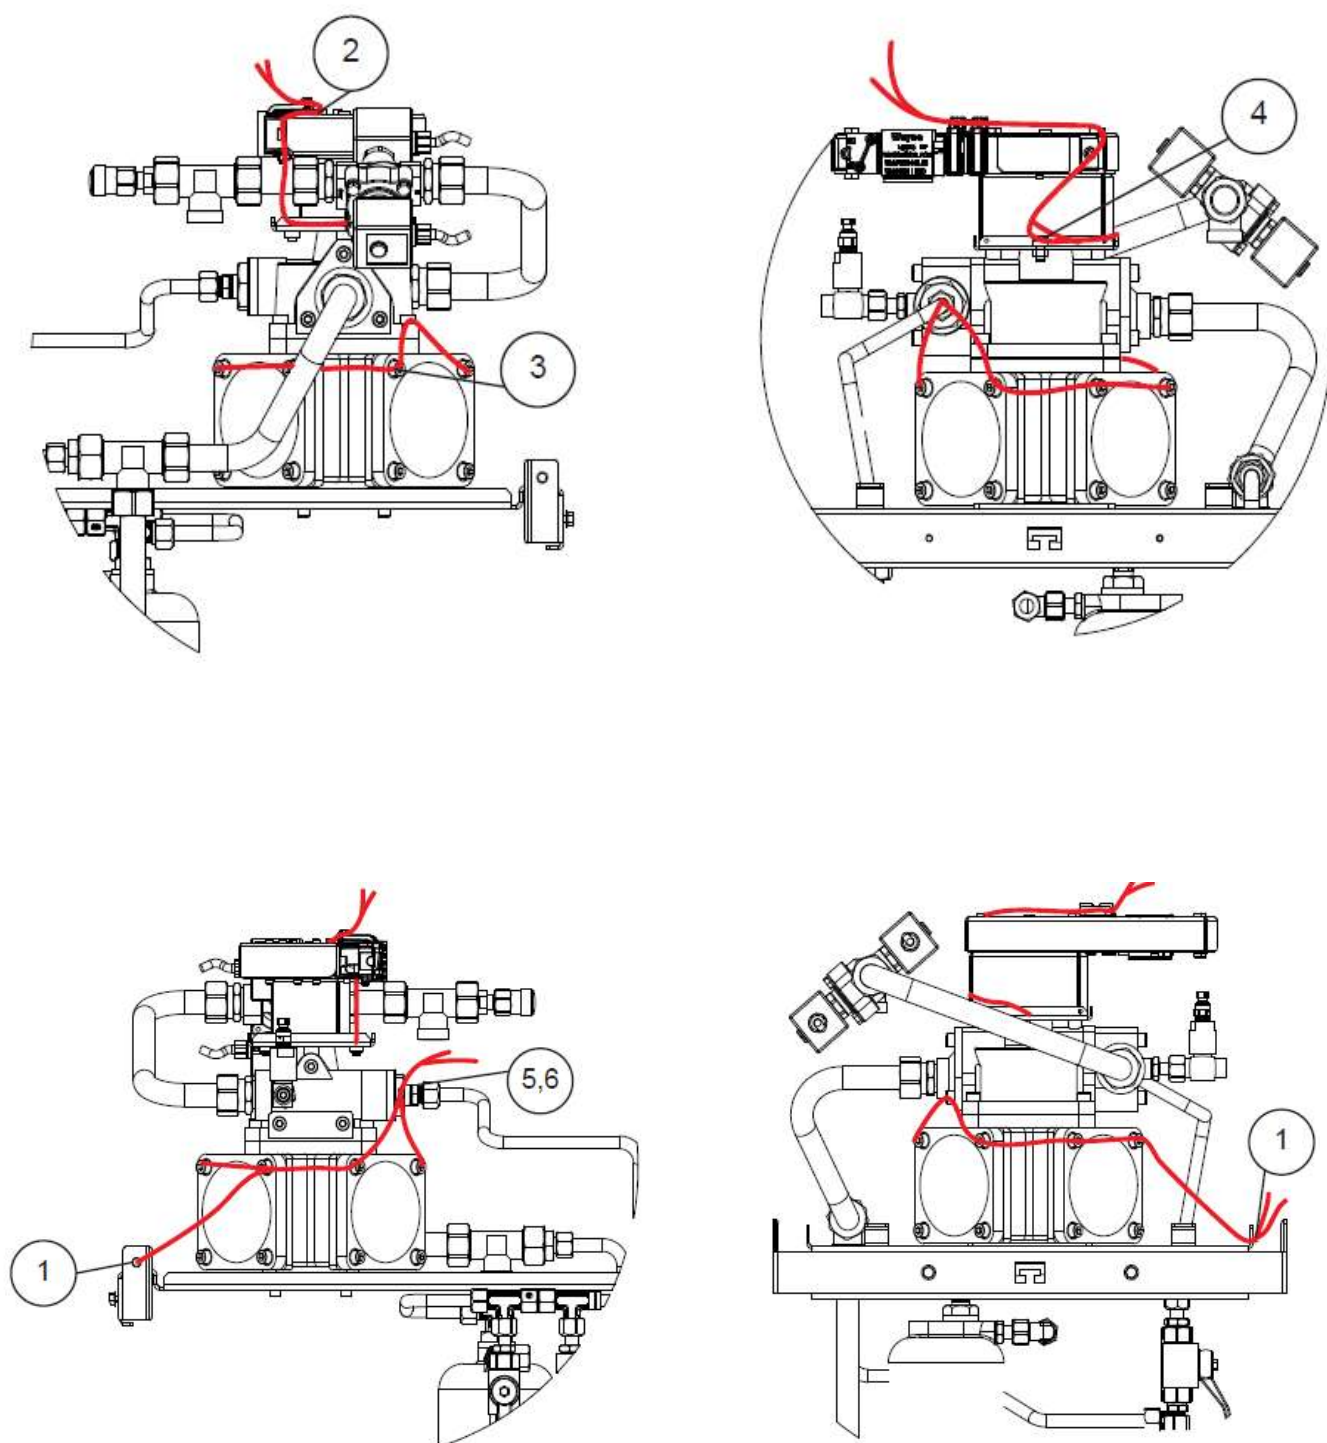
Схема нанесения знака поверки на LPG6000
